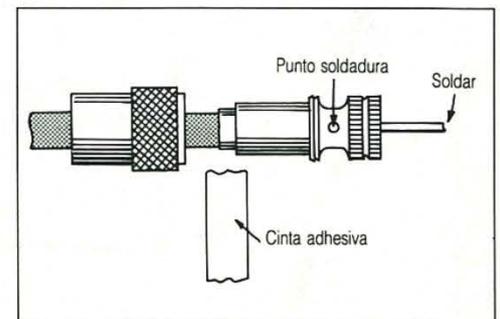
Si se puede dar un punto de soldadura, mejor.
